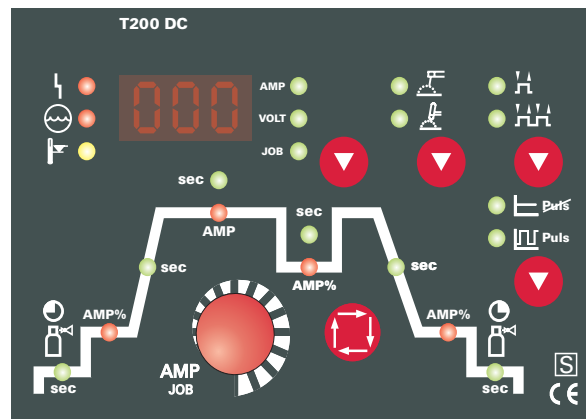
Устройство управления инверторного источника тока EWM для сварки ВИГ TRITON 220 DC PowerSinus
